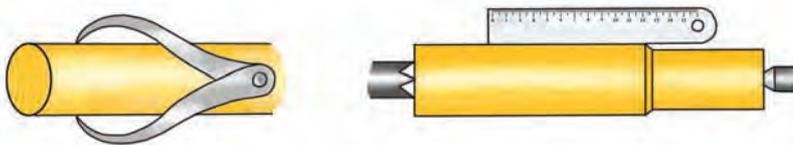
Контроль качества точения: кронциркулем (слева) и линейкой (справа)
